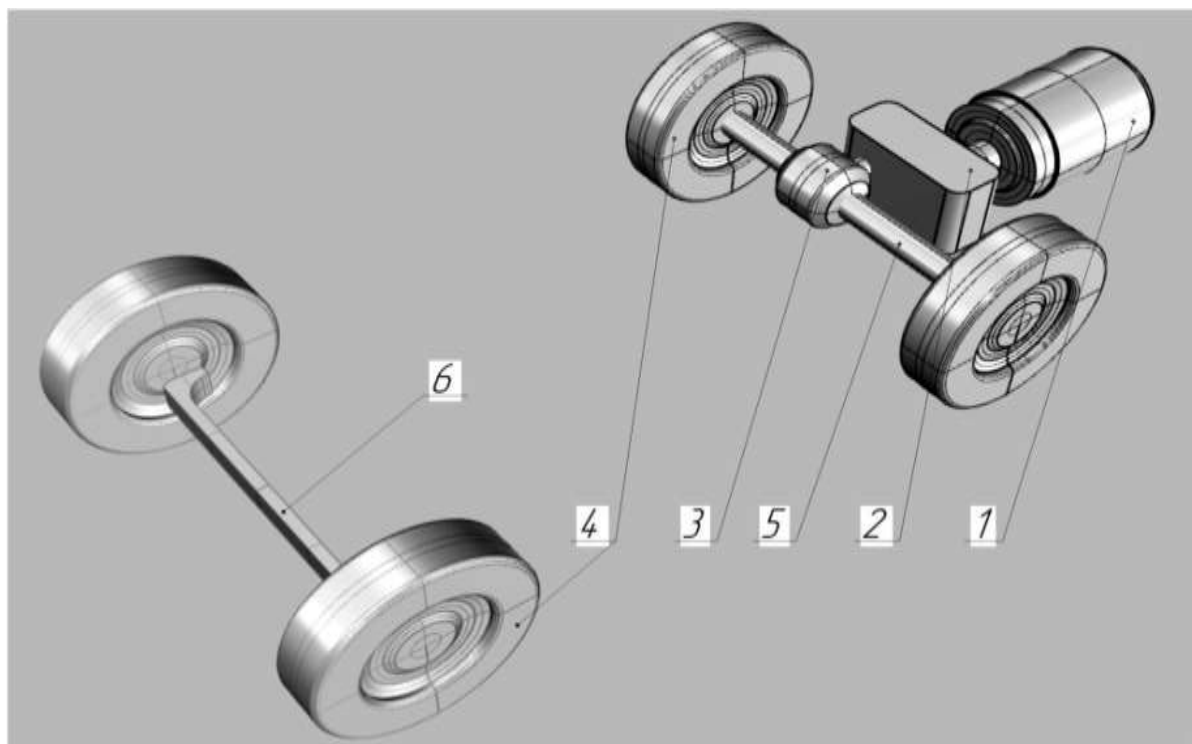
Общий вид привода на задние колеса с двигателем, установленным за осью: 1 – электрический двигатель, 2 – редуктор, 3 – главная передача с дифференциалом, 4 – колесо, 5 – передняя управляемая ось, 6 – задняя ведущая ось
